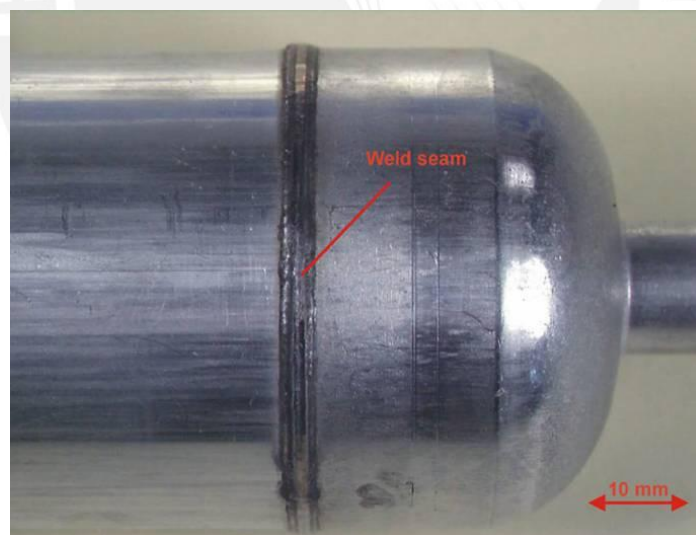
Soldadura circunferencial de dos recipientes para airbag
